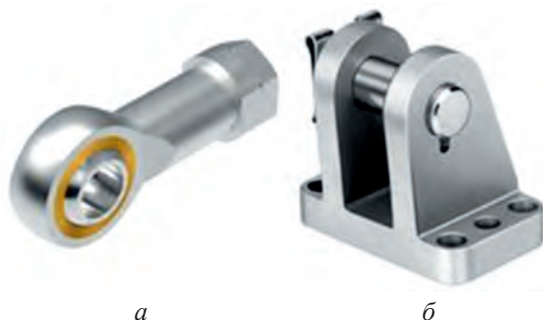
Шарнир: а – на шток; б – опорная стойка
